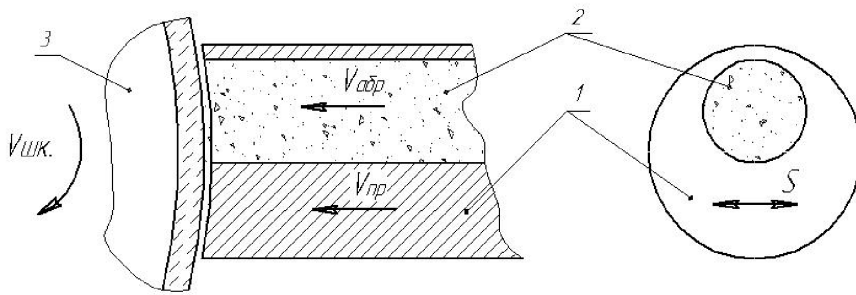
Схема процесса правки шлифовальных кругов свободным абразивом:
